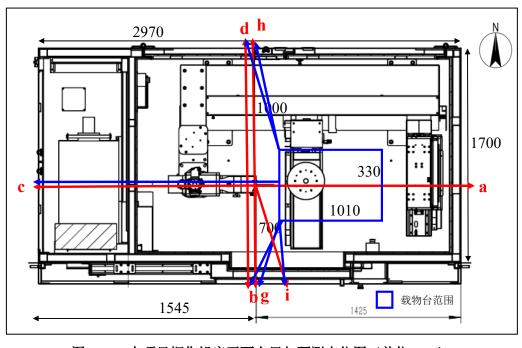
本项目探伤铅房平面布局与预测点位图(单位:mm)
